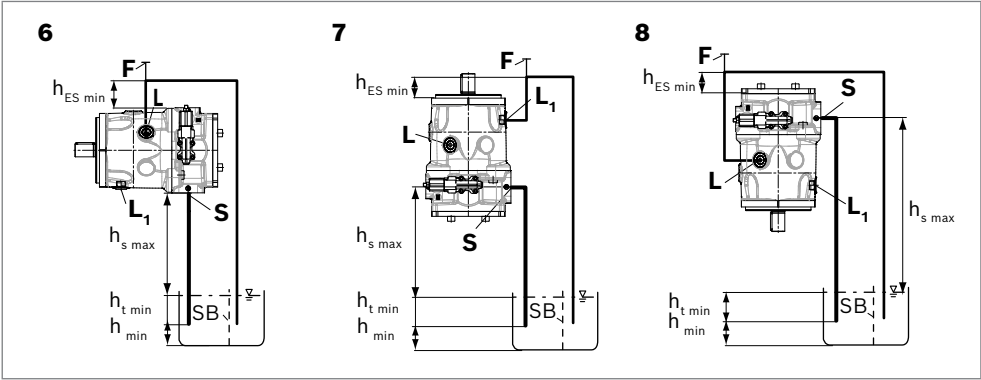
Übertankeinbau A10VZO mit Einbaulage 6–8
